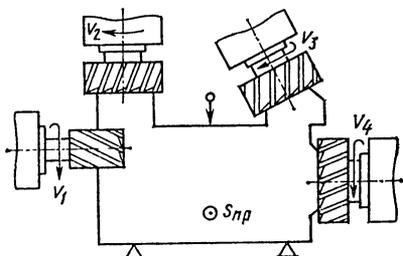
Схема обработки поверхностей на продольно-фрезерном станке
